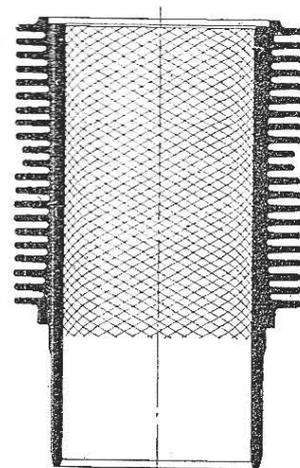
Rodage interne des cylindres avec pièce extensible spéciale
